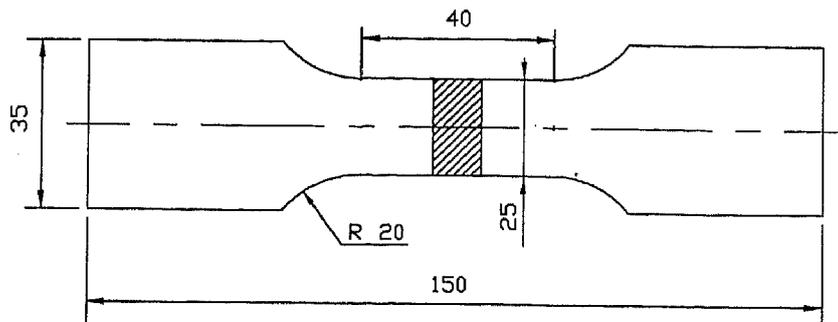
Desenho de provetes que vão ser submetidos ao ensaio de tracção (na soldadura)
